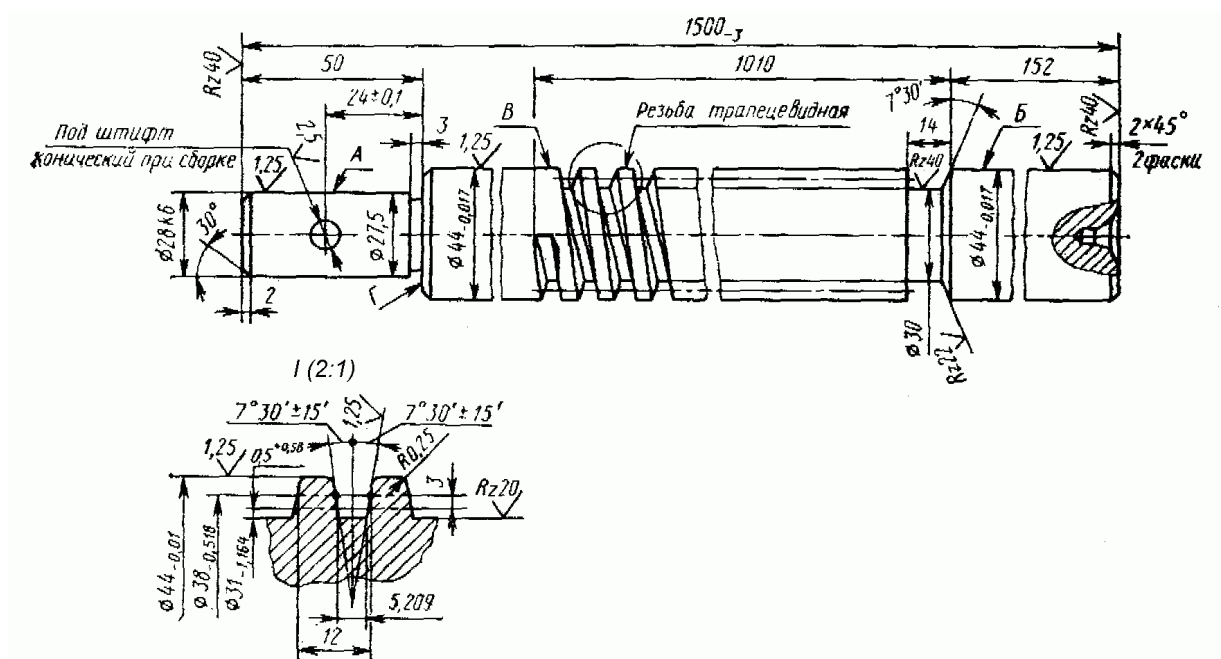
Ходовой винт токарного станка 16К20
